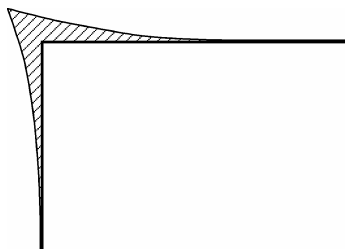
Схема формирования «недореза» на поверхности заготовки
